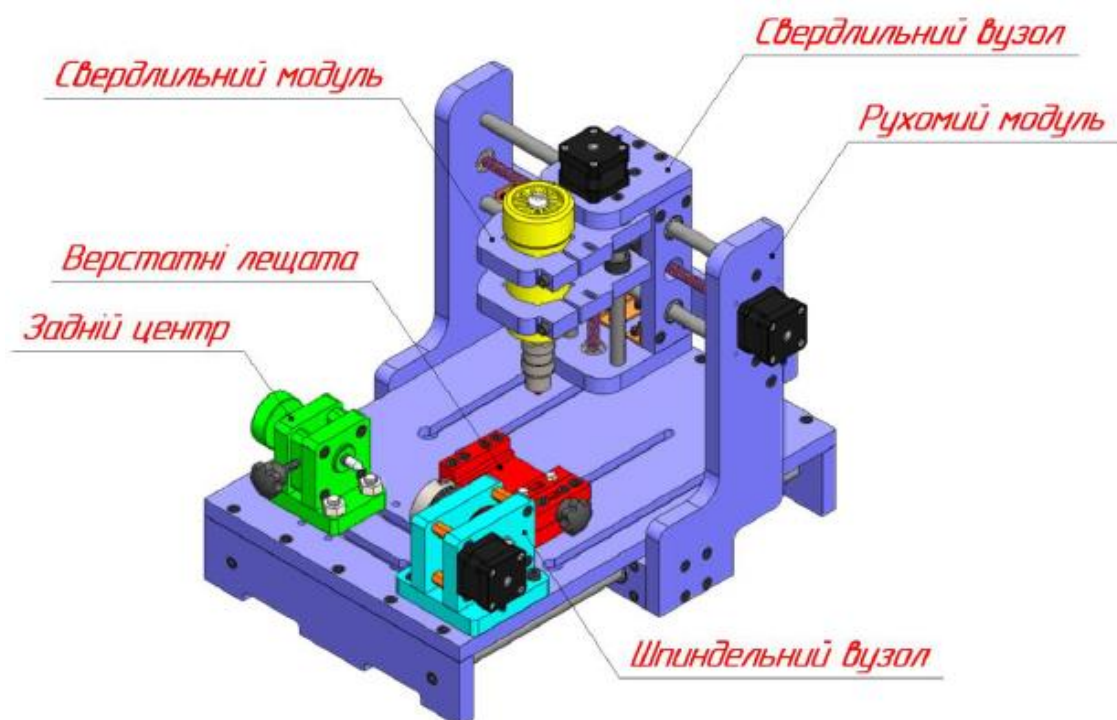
Вертикально-фрезерний верстат в сборі
